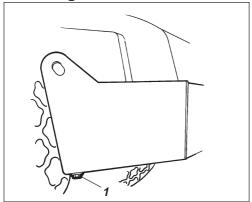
Réservoir de carburant 1. Bouchon de vidange
